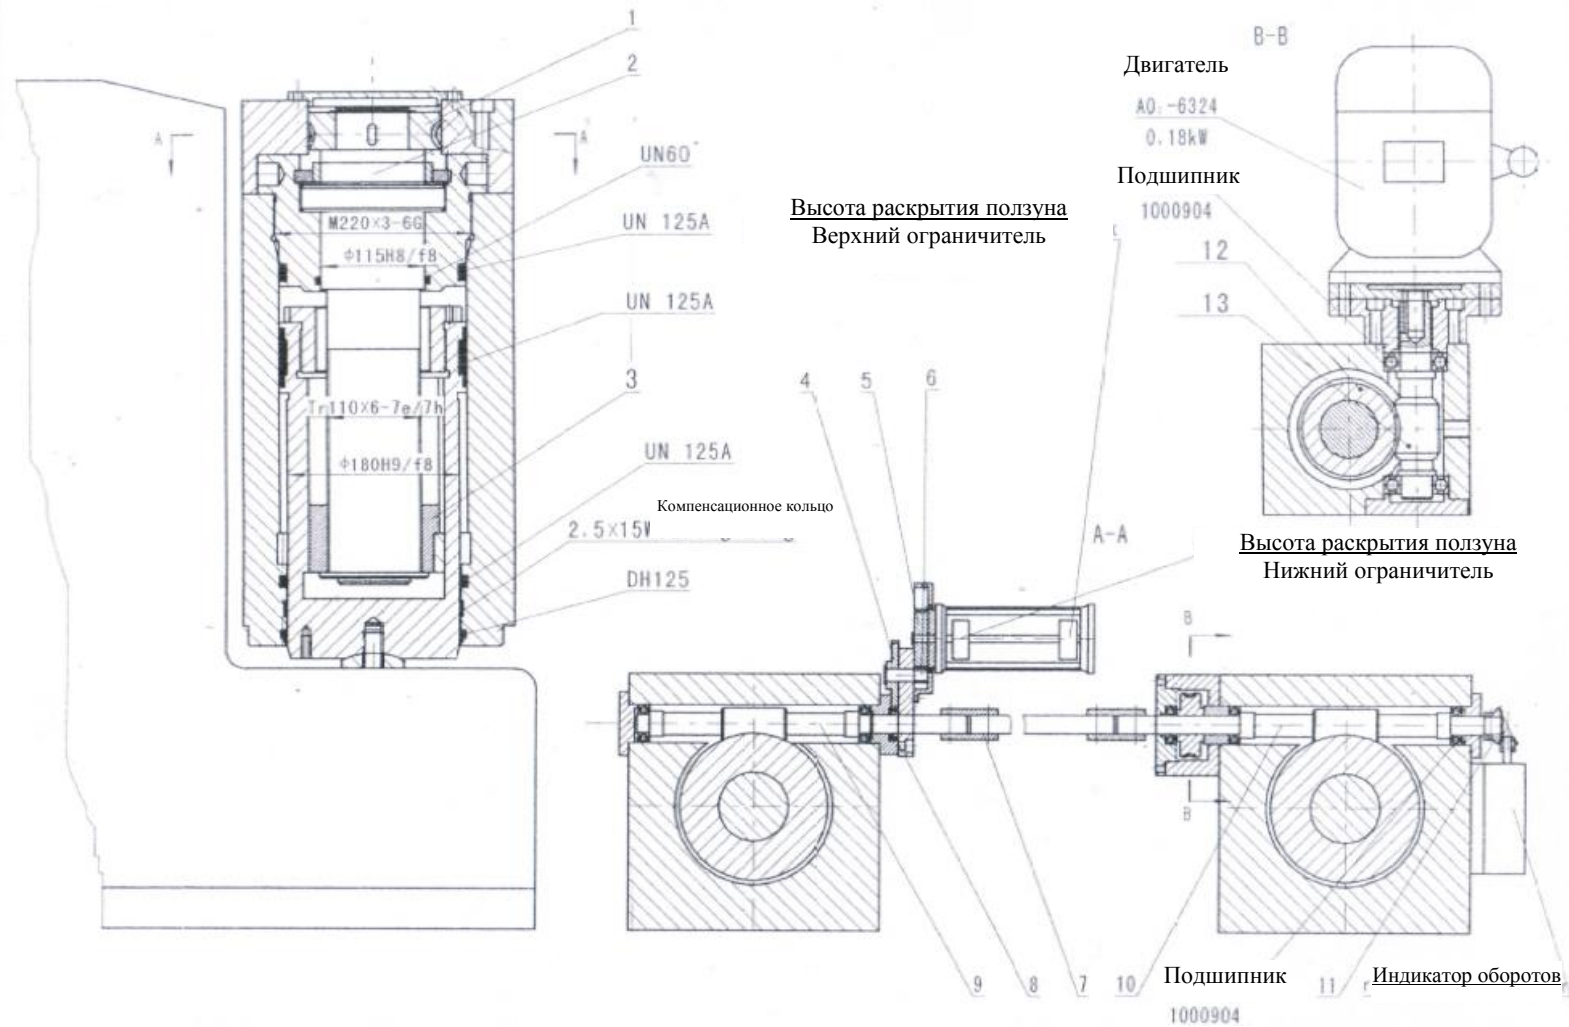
Схема гидроцилиндра и механизма установки координаты по оси «У»
